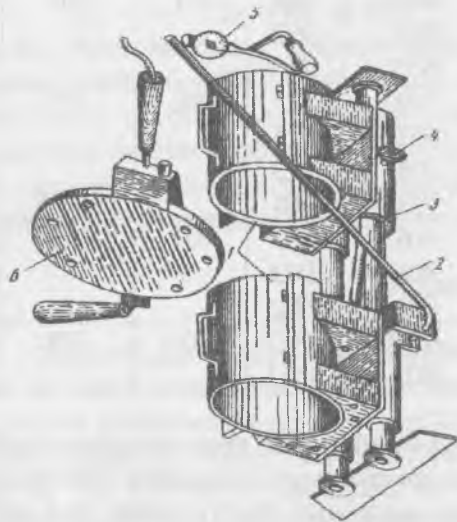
Центруючий пристрій для зварювання полімерних труб
